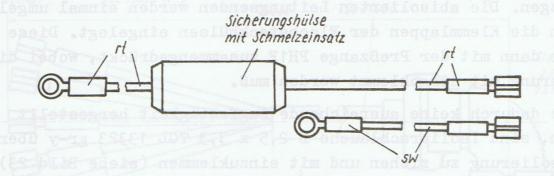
Kabelvorbereitung Einleiterprinzip nur für Montage in Fahrzeugen
